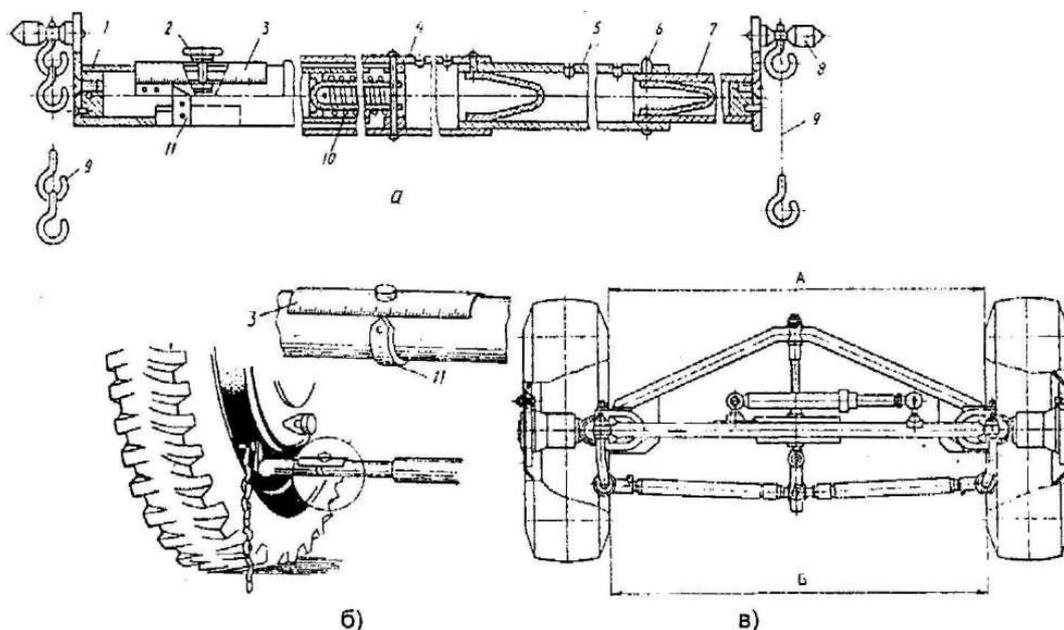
Проверка сходимости передних колес машин: а - линейка КИ-650; б - установка линейки; в - замер сходимости колес; 1- подвижная труба; 2 - винт; 3 - шкала; 4 - наружная труба; 5 - промежуточная труба; 6 - фиксатор; 7 - удлинитель; 8 - контактный наконечник; 9 - цепочка; 10 - пружина; 11 - стрелка; I - места замера сходимости колес; А - расстояние между задней частью колес; Б - расстояние между передней частью колес
